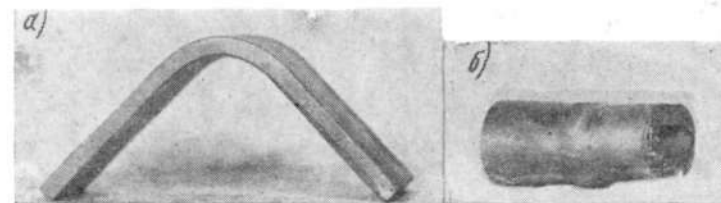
Образцы, испытанные на стойкость против межкристаллитной коррозии: а — плоские сварные соединения; б — трубные сварные соединения.
